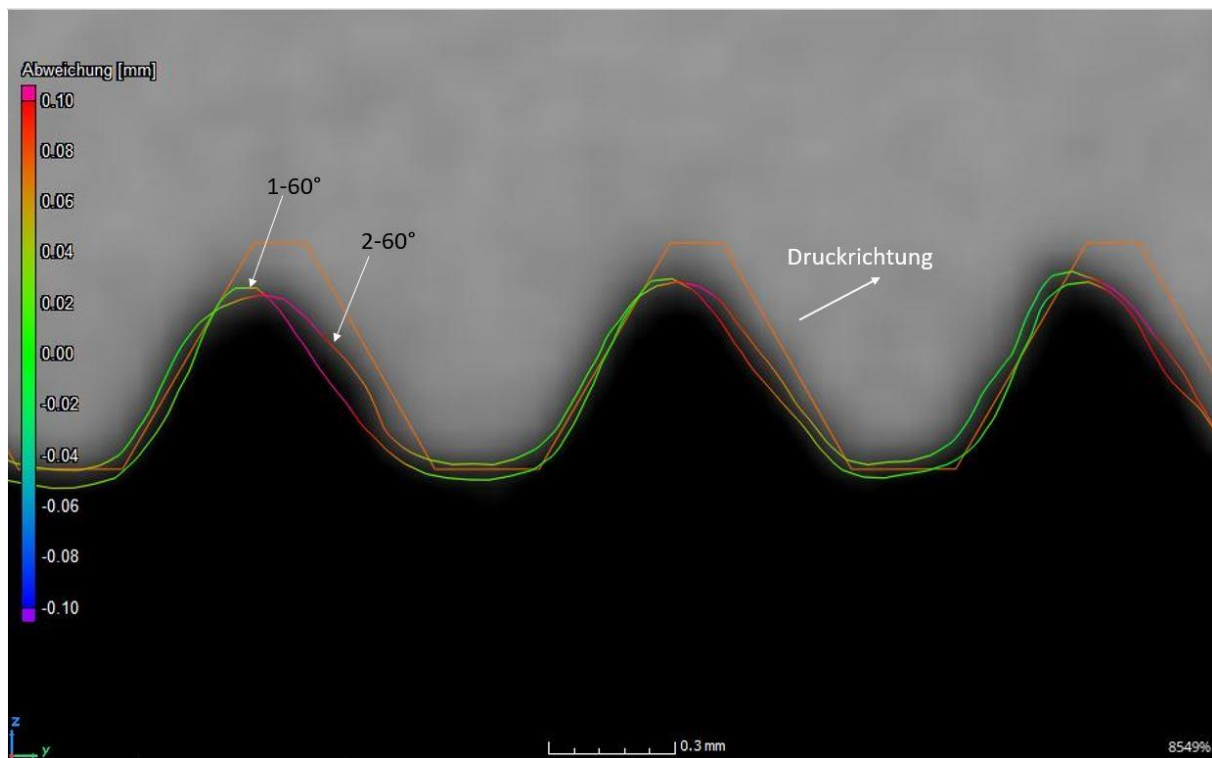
Details der Hängenden Gewindeflanke Proben 1-60° und 2-60°
